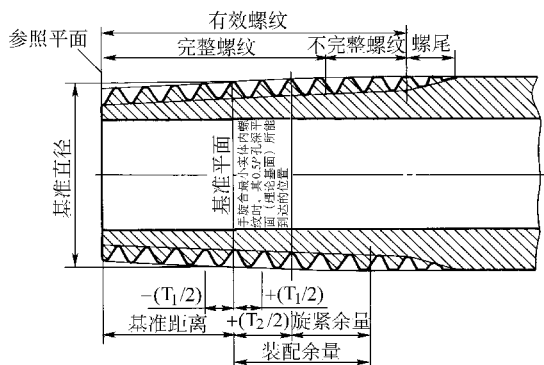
圆锥外螺纹各主要尺寸的分布位置
